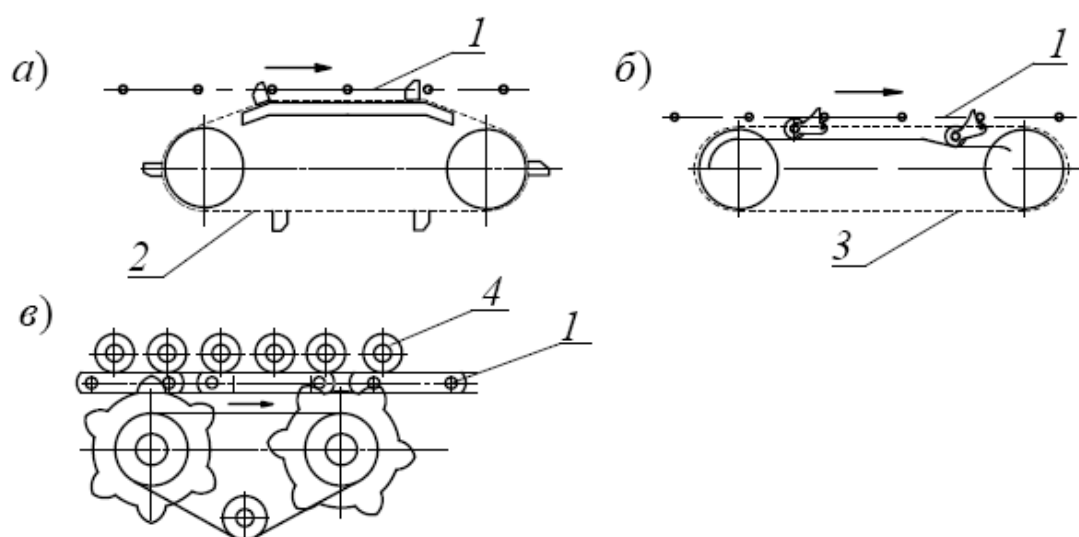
Схемы промежуточных приводов пластинчатых конвейеров: *а* – привод гусеничного типа с жесткими ведущими кулаками и поджимной шиной; *б* – привод гусеничного типа с управляемыми ведущими кулаками и профильной шиной; *в* – привод со звездочками с цевочным зацеплением с тяговой цепью; *1* – тяговая цепь конвейера; *2* – приводная цепь с ведущими кулаками; *3* – приводная цепь с ведущими управляемыми кулаками; *4* – прижимные ролики
